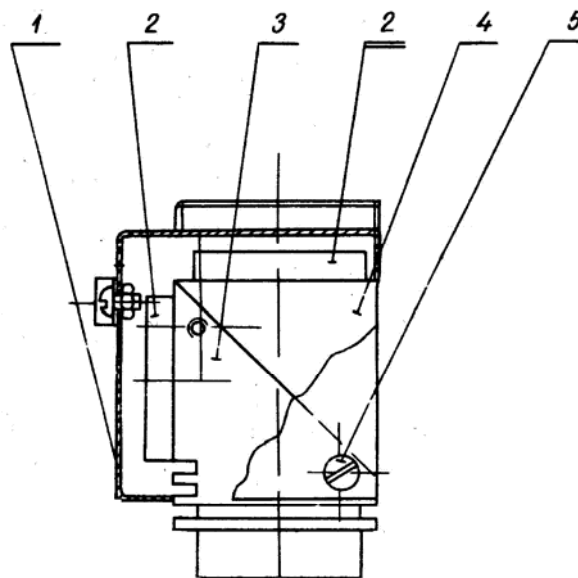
Конструкция комбинированного преобразователя на средах свинец-медь. 1 - защитный корпус; 2 - пьезоэлементы; 3 - контактная часть звукопровода; 4 - торцевая часть звукопровода; 5 - крепление защитного корпуса к звукопроводу.
